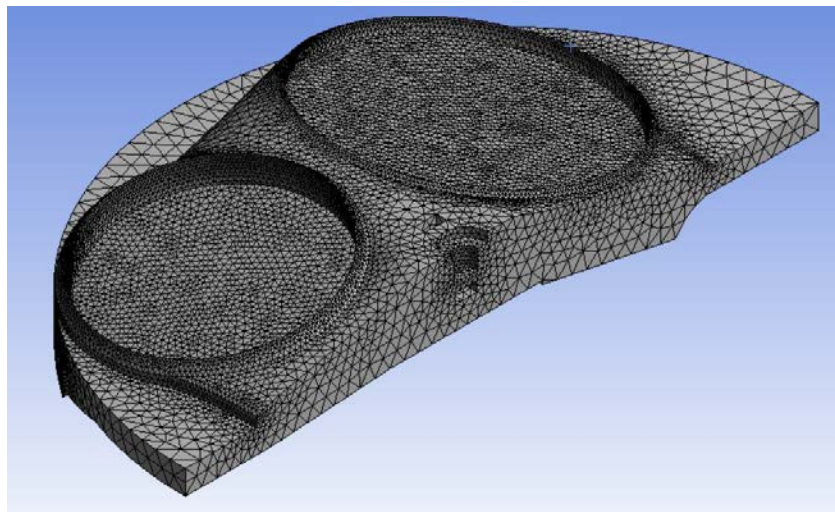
Immagine della mesh nella zona della camera di combustione
